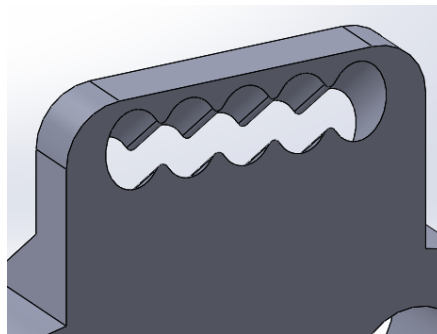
Acoplador de la mano. Detalle del soporte de los tubos guía
